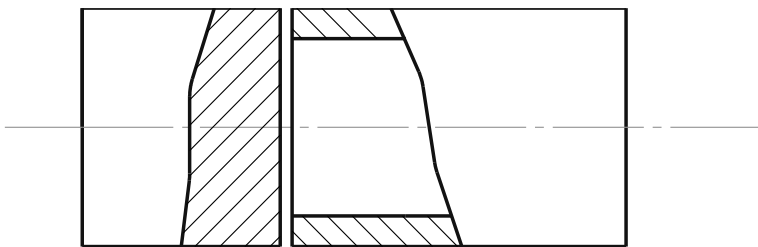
Сварка трубы со стержнем встык
